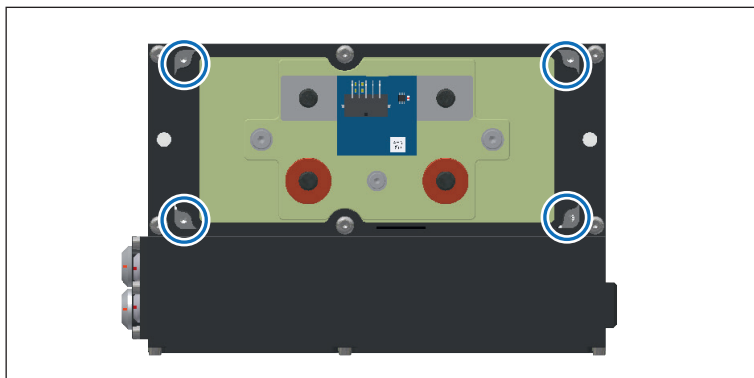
HV BM 1.2, M3-Gewindebohrungen im Modulgehäuse
